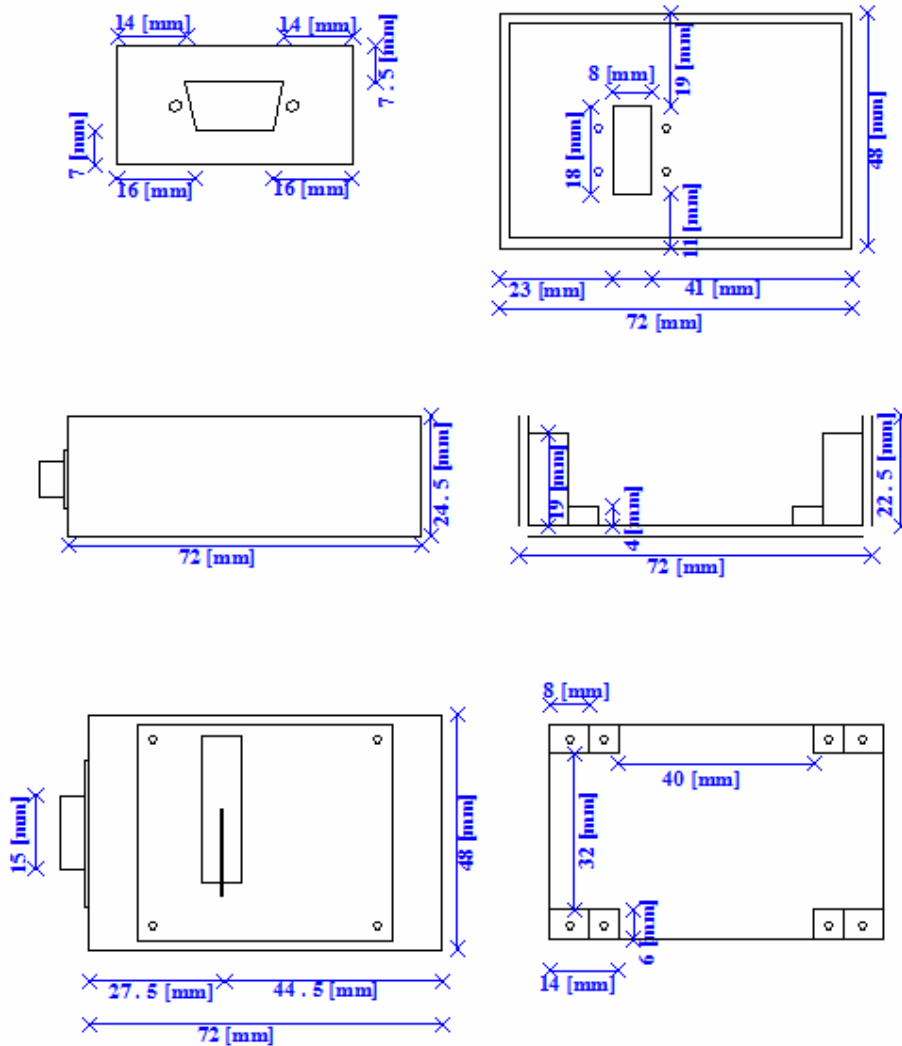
Dimensiones finales y diseño mecánico del Sensor de Sol.
